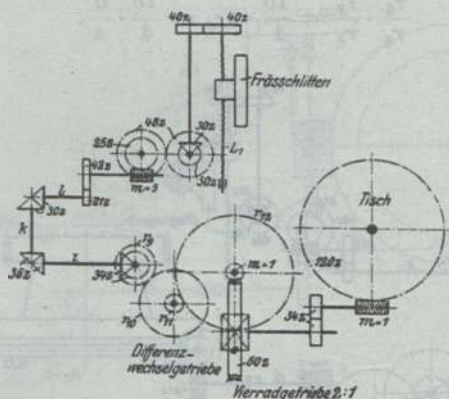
Antrieb der Zusatzbewegung für Schraubenräder.
